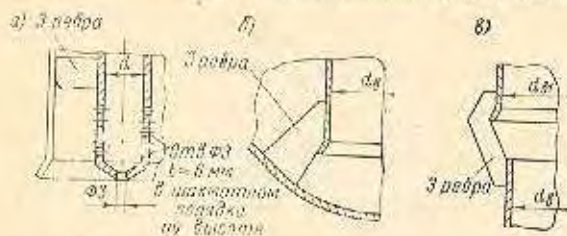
Основные конструктивные узлы сварных барботеров типа газлифта: а — видевая часть газовой трубы; б — нижнее крепление подъемной трубы газлифта; в — крепление подземных труб газлифта между собой
